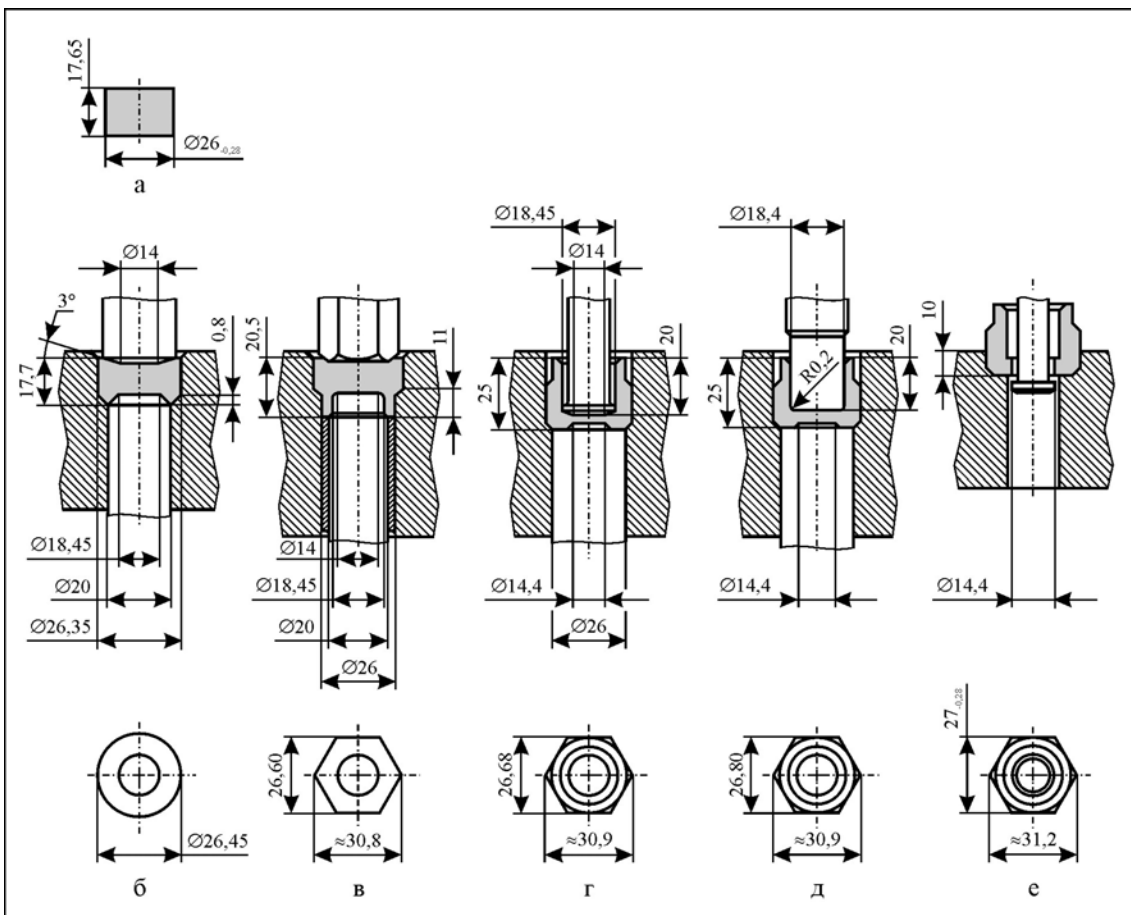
Переходи та налагодження робочого інструмента при штампуванні накладної гайки M20 × 1,5: а – вихідна заготовка; б – перша позиція; в – друга позиція; г – третя позиція; д – четверта позиція; е – п'ята позиція (див. табл. 7.1)
